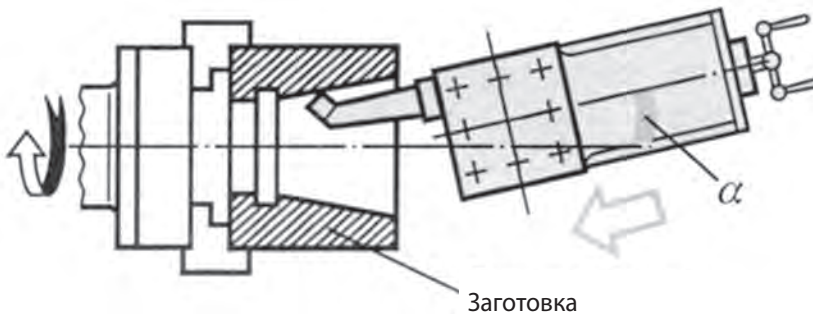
Обробка внутрішнього конуса перевернутим розточувальним різцем
